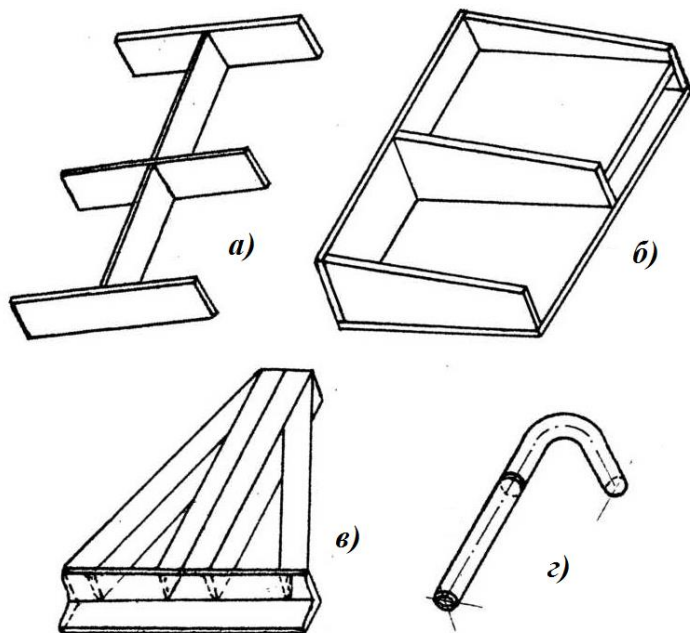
Примеры сваренных узлов, собираемых при помощи приспособлений УСПС: а) рамка; б) кожух; в) стойка; г) труба с коленом.
